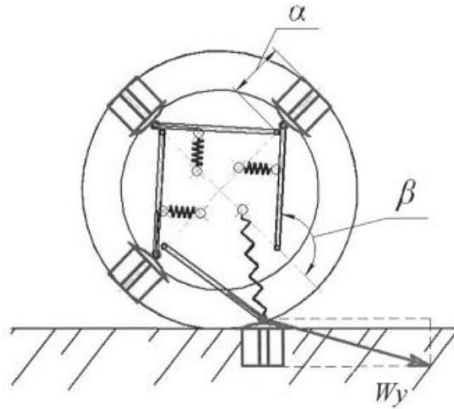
Колісний рушій при русі машини, профільний вид
